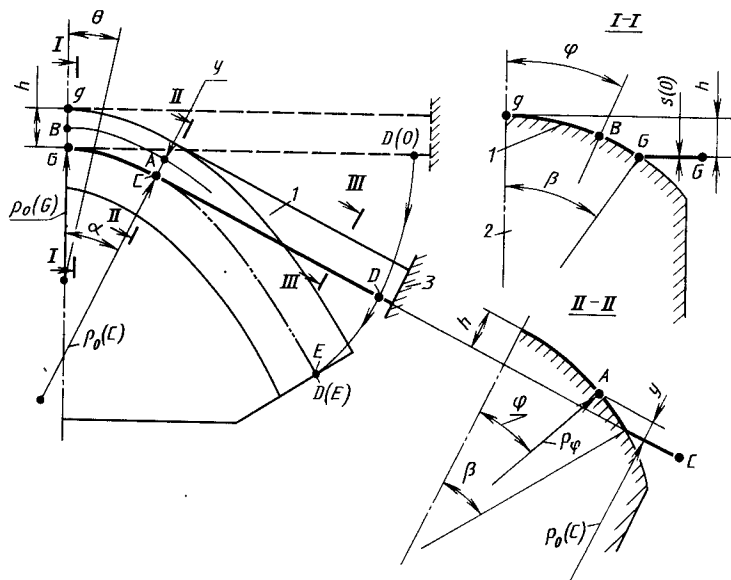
Схема обтяжки широким листом инструмента с двояковыпуклой поверхностью: 1 — заготовка; 2 — пуансон; 3 — захват
